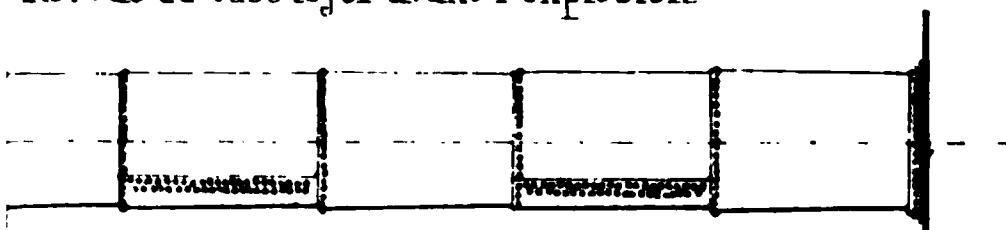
Vue du tube foyer après l'explosion. (Côté Ouest)
